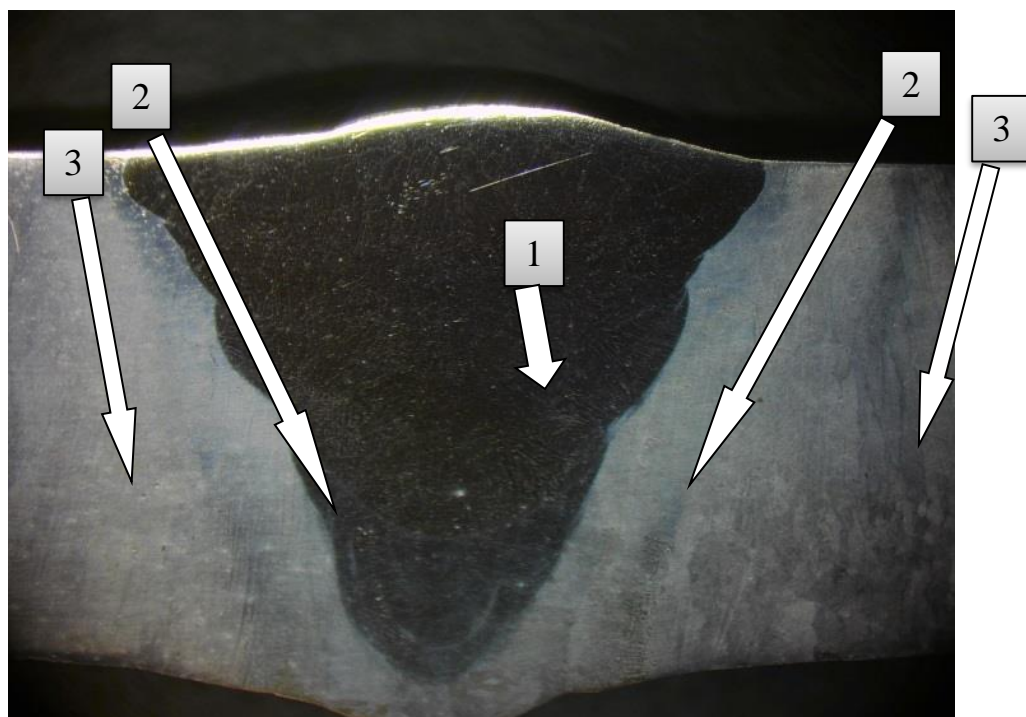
Схема разделения сварного шва на участки
